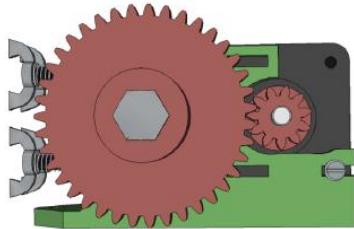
Colocación Montaje del motor y ensamblado de los engranajes (paso 3)
